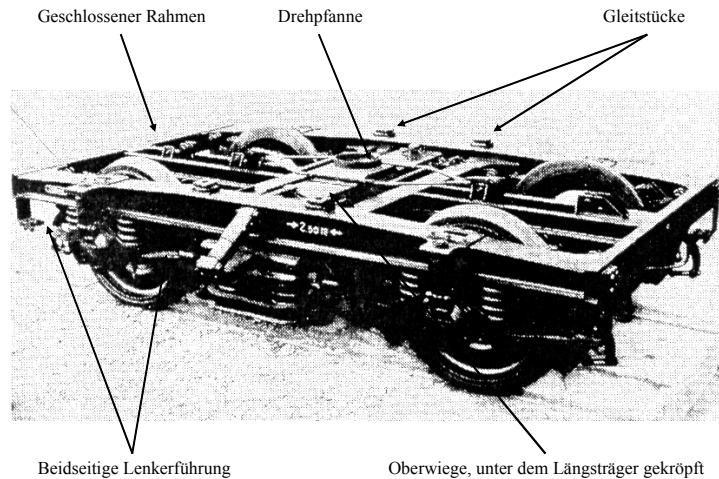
Fahrwerk mit Wiegenkonstruktion (MD36-Fahrwerk)
